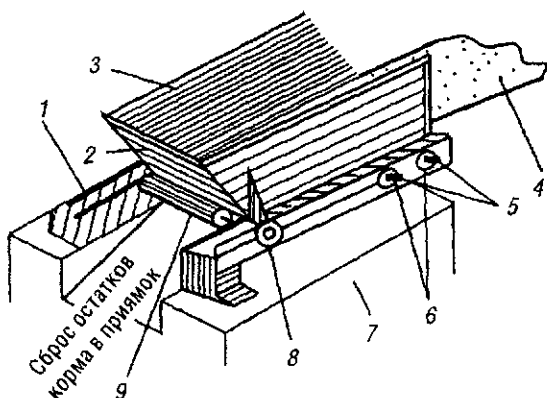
Натяжная станция с загрузочным бункером транспортера-раздатчика кормов ТВК-80Б: 1 – боковина опорной рамы; 2 – дверца бункера; 3 – приемный бункер; 4 – лента; 5 – натяжные винты; 6 – контргайки; 7 – фундамент; 8 – вал барабана; 9 – натяжной барабан
